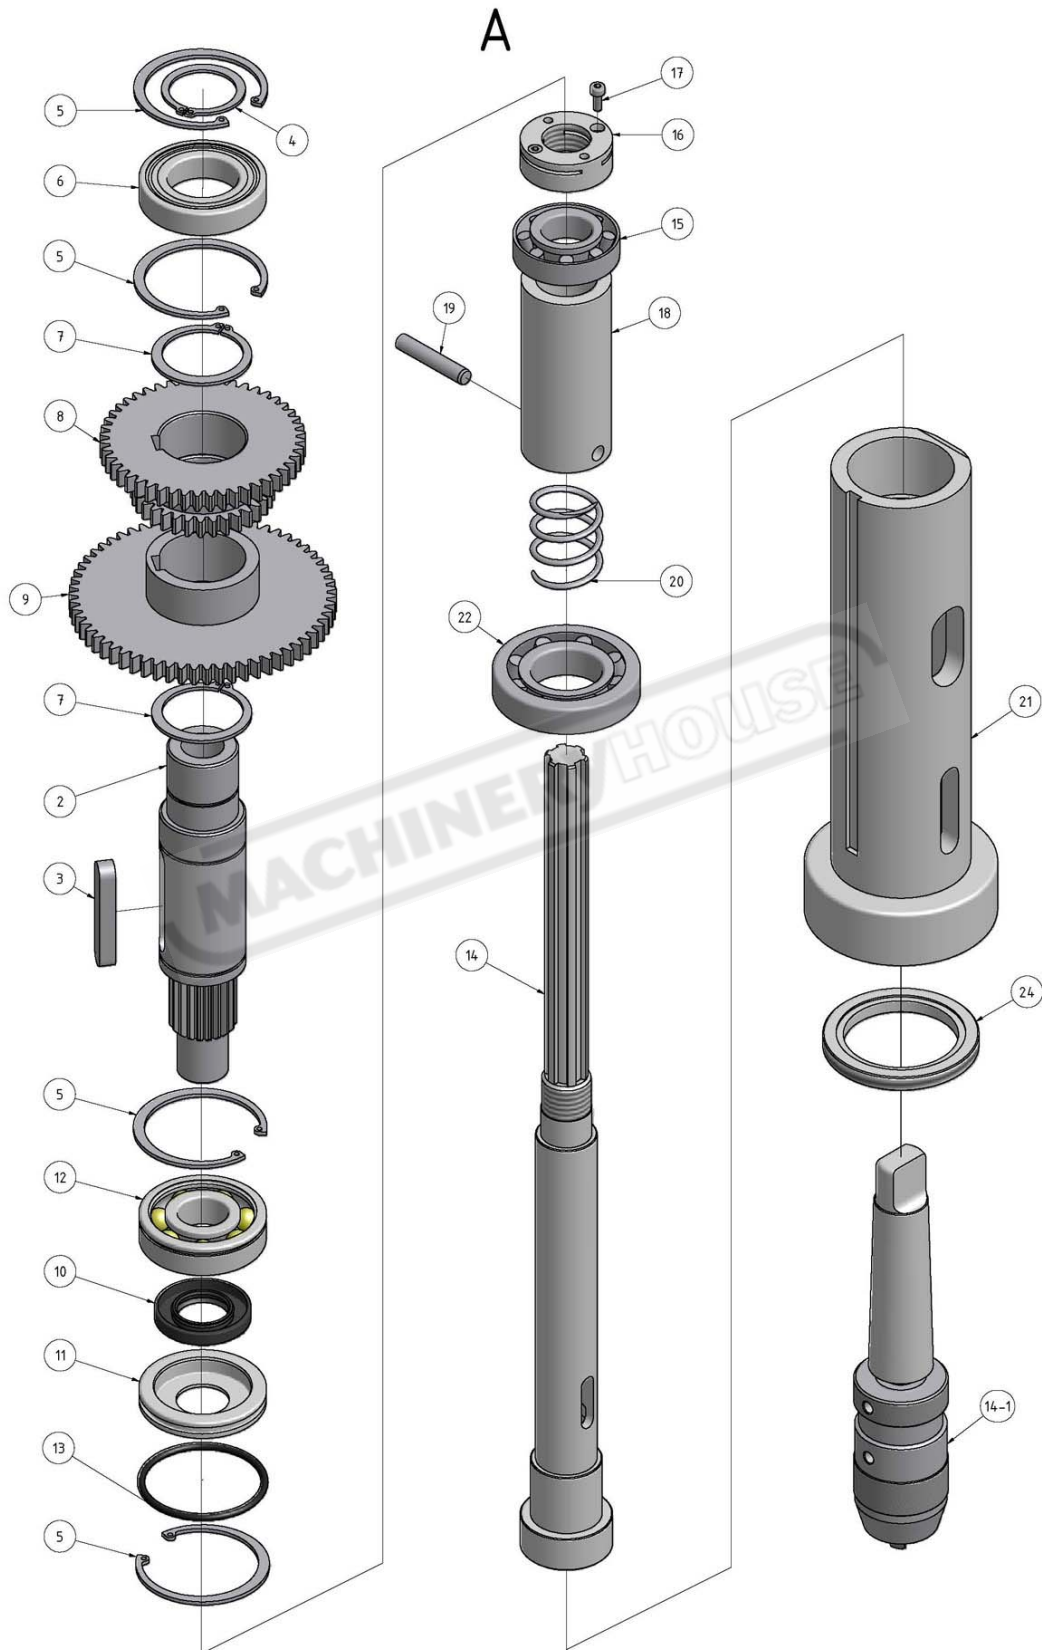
Bohrkopf 1 von 9 - Drilling head 1 of 9
